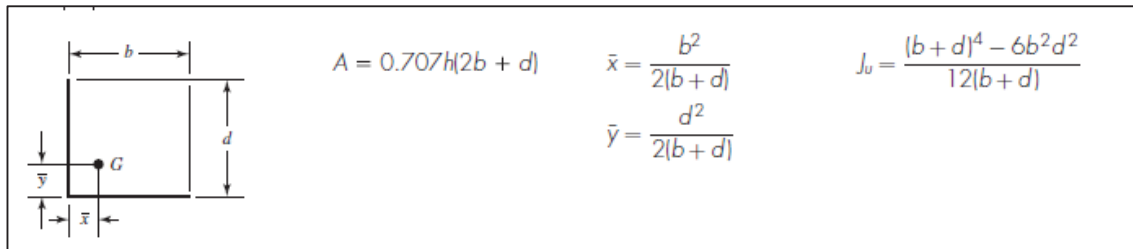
Propiedades torsionales de las soldaduras de filete.
